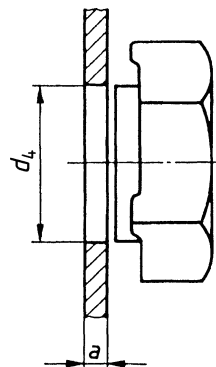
Anschlussmaße (Mutter noch nicht angeschweißt)
